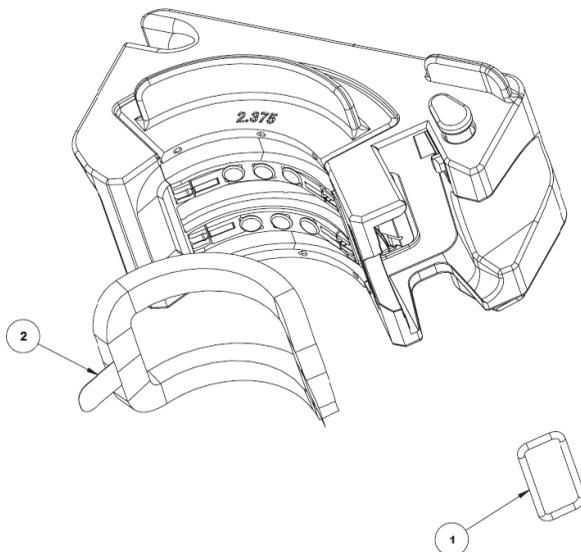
Vista detallada de las suelas (zapatas) SFA1-AUTO y SFA1-SMALL
